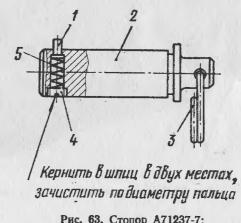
Стопор А71237-7: 1— стопор А51620-47; 2— палец А51621-50; 3— кольцо А51203-175; 4— пробъв А52150-12; 5— пружина А51230-109
